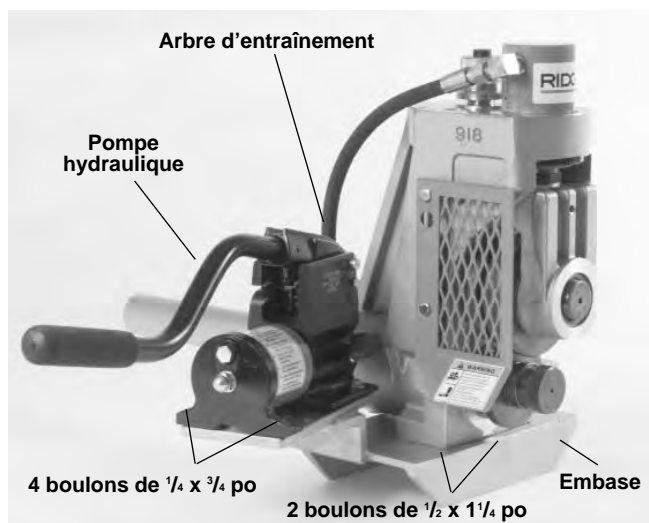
Rainureuse à galets n° 918 sur embase de machine à fileter n° 535
